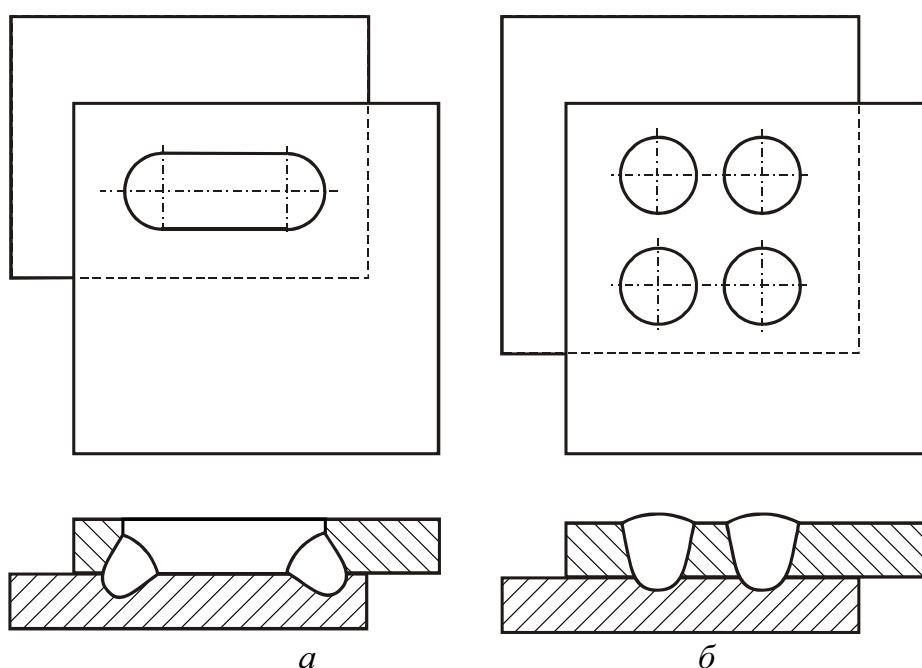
Пререзное и электрозаклёпочное сварное соединение
